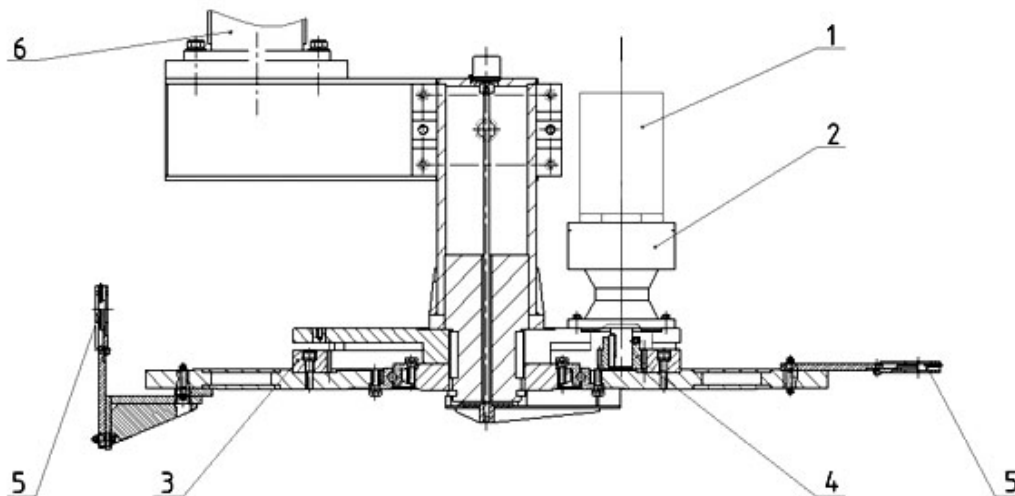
Магазин инструментов на 28 посадочных гнезд под различный инструмент.
